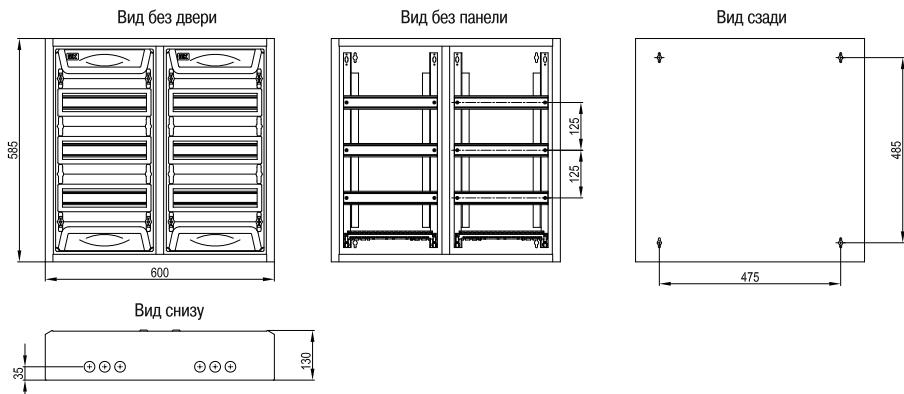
Габаритные и установочные размеры металлокорпусов
